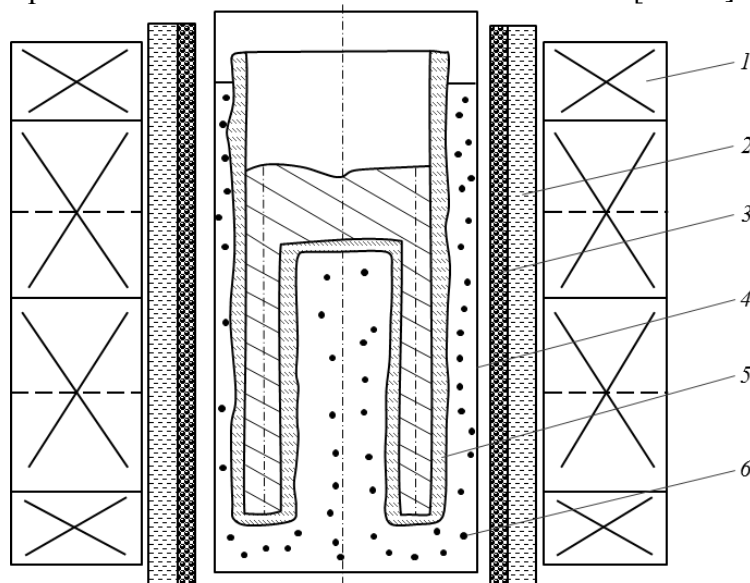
Цилиндрический однополюсный электромагнитный индуктор: 1 – фазные катушки; 2 – водоохлаждаемый корпус; 3 – печь подогрева формы; 4 – металлическая опока; 5 – керамическая литейная форма; 6 – формовочный наполнитель
